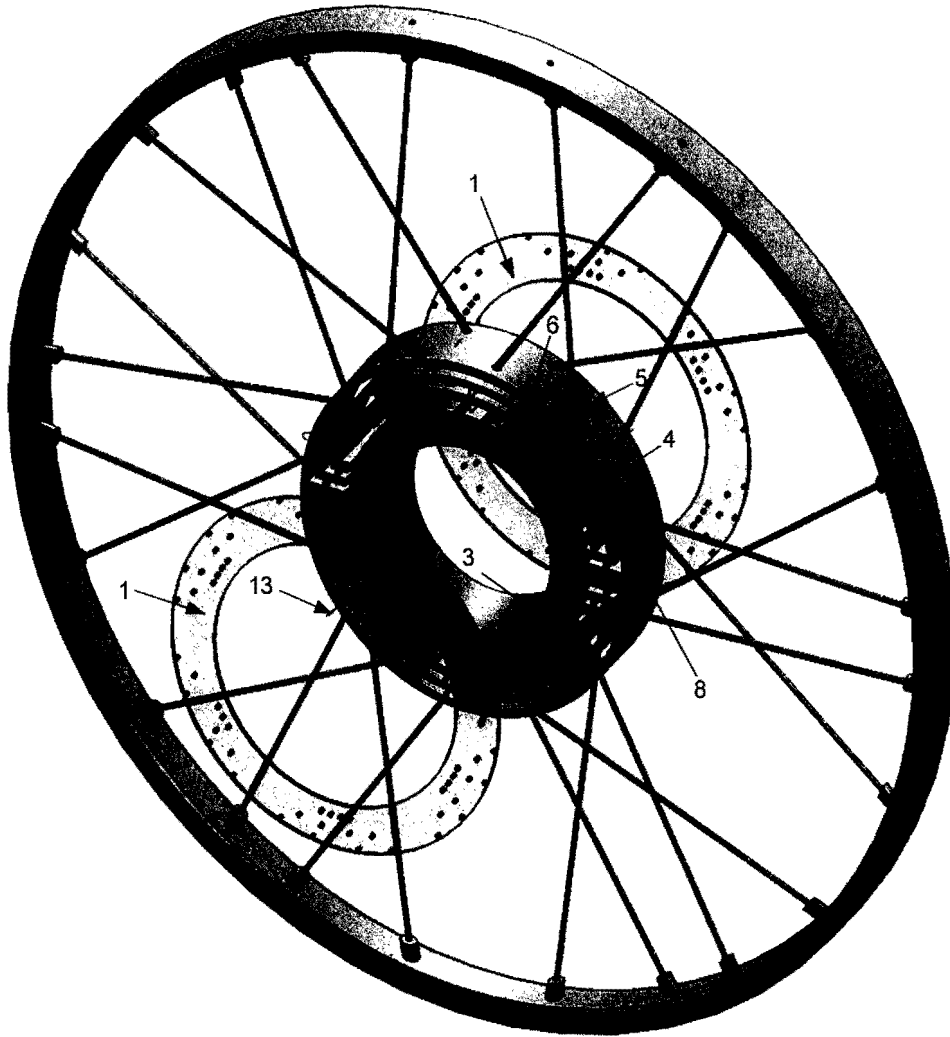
Vederea în spațiu a roții de bicicletă cu mașina electrică încorporată.
